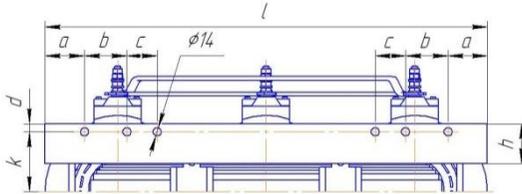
б – Установочные размеры трансформатора (вид снизу).
